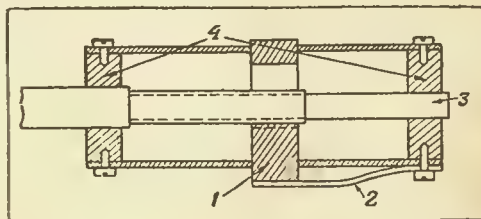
Супорт т. Трушина: 1—полукайка; 2—пружина, сцепляющая полукайку с резьбой винта; 3 — направляющая с винтом; 4 — направляющие втулки
